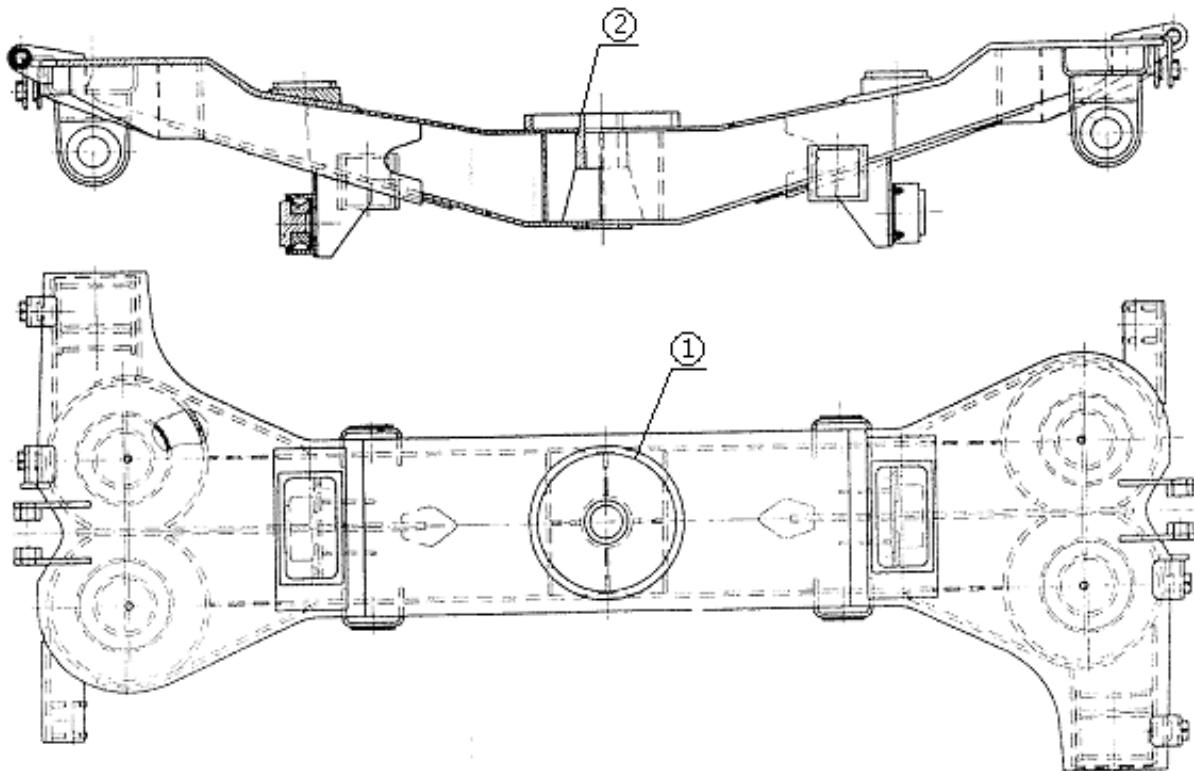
Основные дефекты надрессорного бруса безлюлечных тележек модели 68-4095, 68-4096 и модели 68-4075, 68-4076, ремонтируемые сваркой или наплавкой
